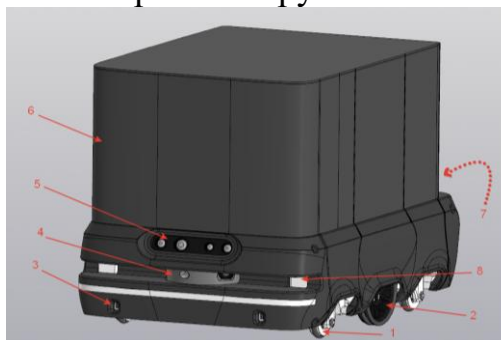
Мобильный колёсный робот для доставки посылок: 1- опорные колёса; 2 – ведущие колеса; 3 - датчик препятствий; 4 - лидар; 5 - блок камер и инфракрасных датчиков; 6 - грузовой контейнер; 7 – система автоматического управления; 8 – фары
